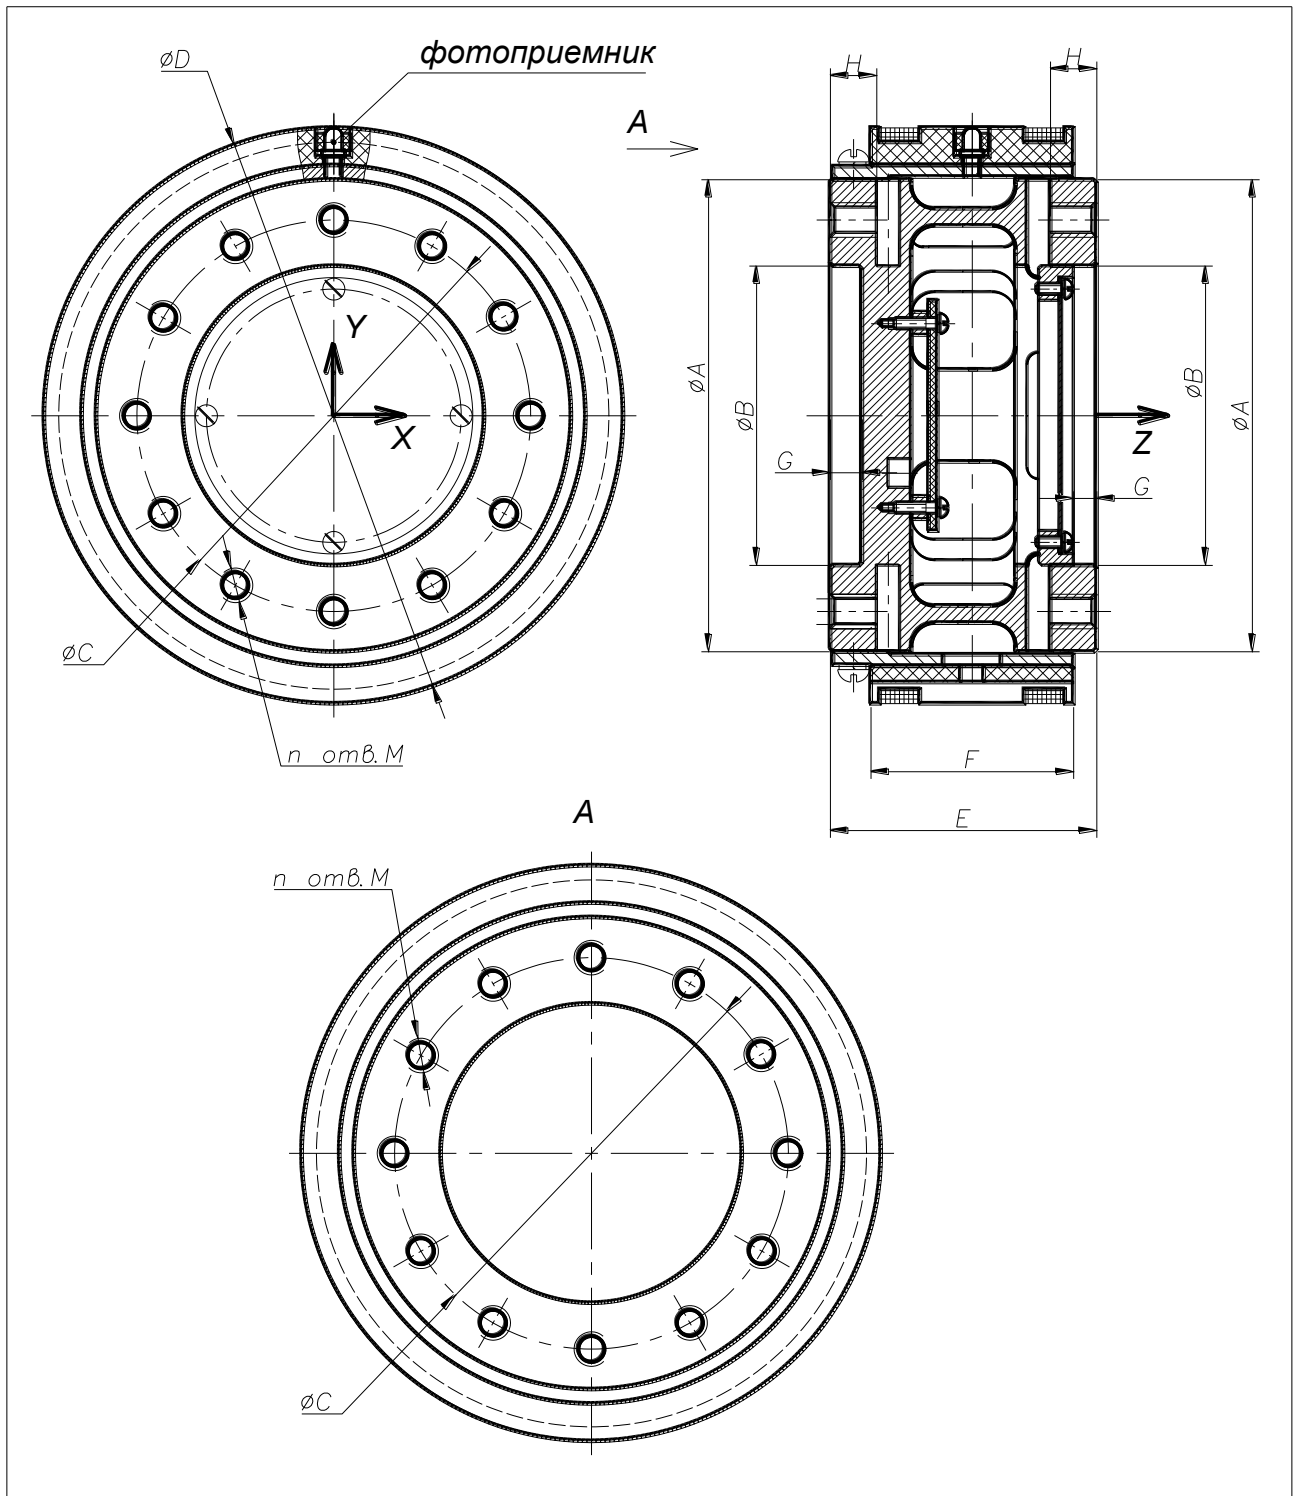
Датчик шестикомпонентный М46. Ротор. Габаритные и установочные размеры, мм
